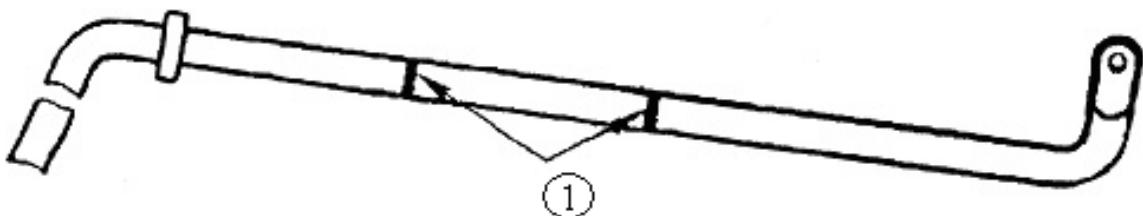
Дефект рычага расцепного, ремонтируемый сваркой
